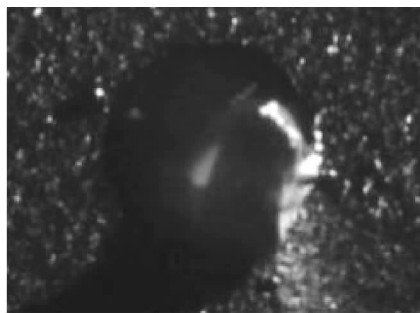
焊接速度为 1.5 m/min 的熔池原始图像
